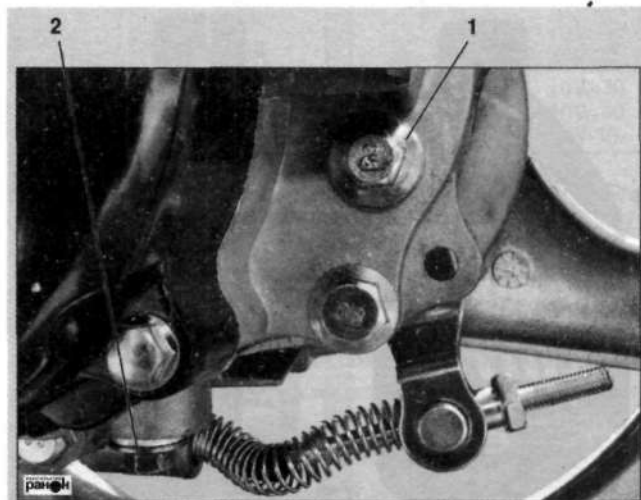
Расположение заливного (контрольного) отверстия: 1 – заливное (контрольное) отверстие редуктора; 2 – сливное отверстие редуктора
